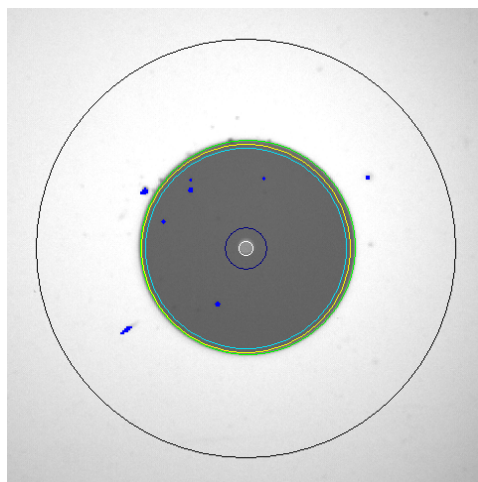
La inspección automática brinda a los técnicos un resultado de aprobado o desaprobado.
